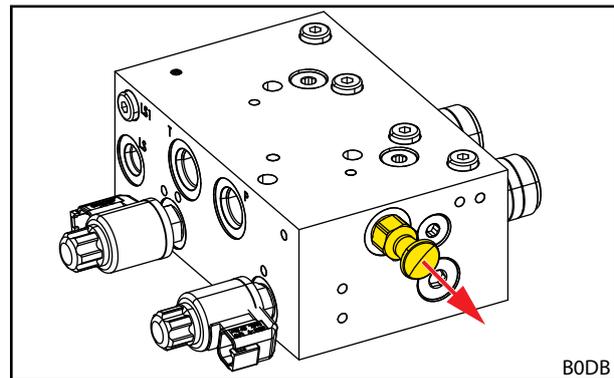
Druckentlastungsventil am REAL³-Ventil herausziehen
